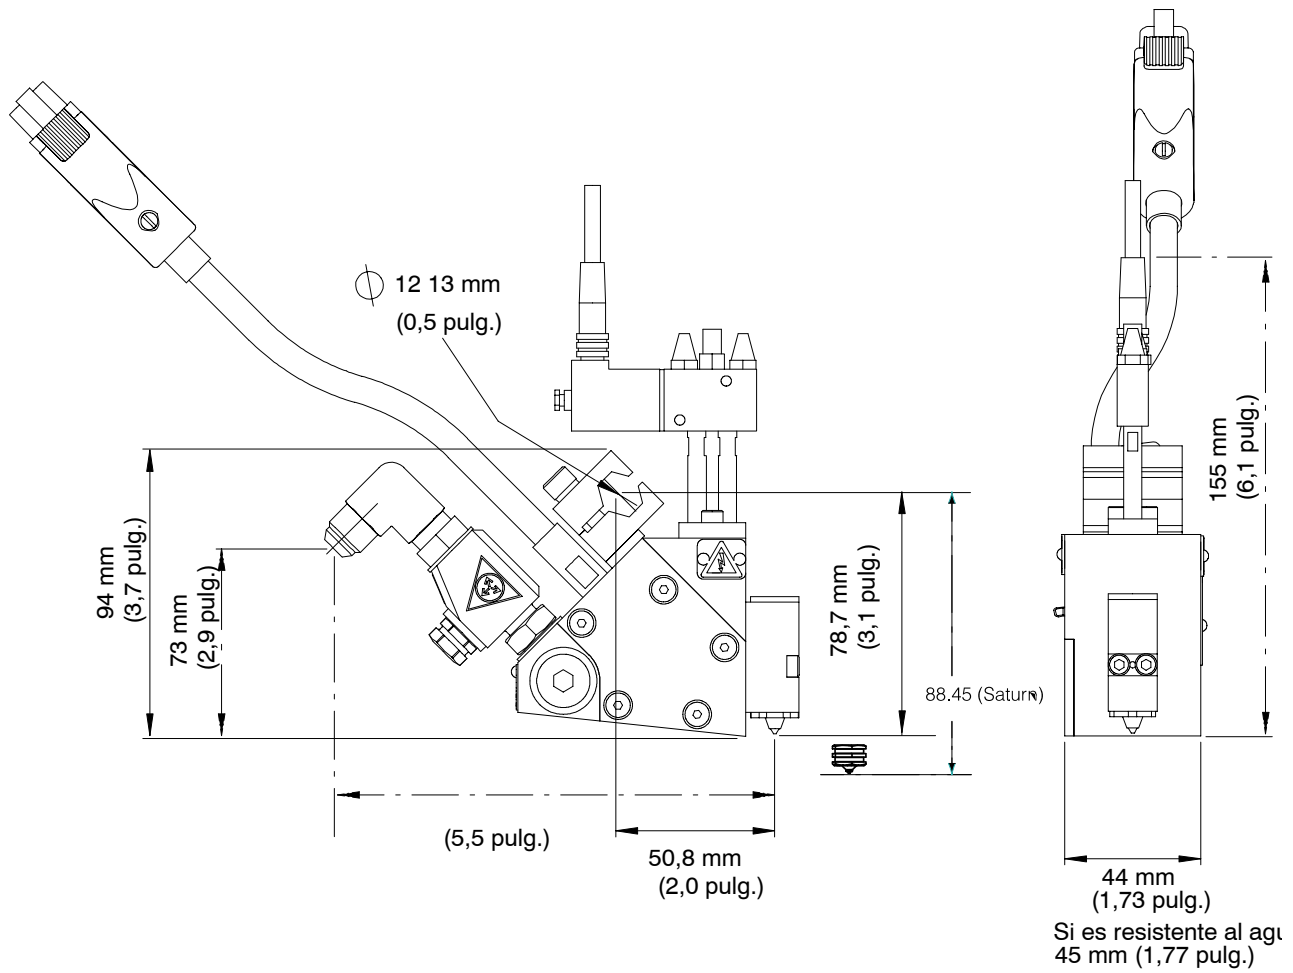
Dimensiones de una pistola configurable de un módulo con una electroválvula SD
